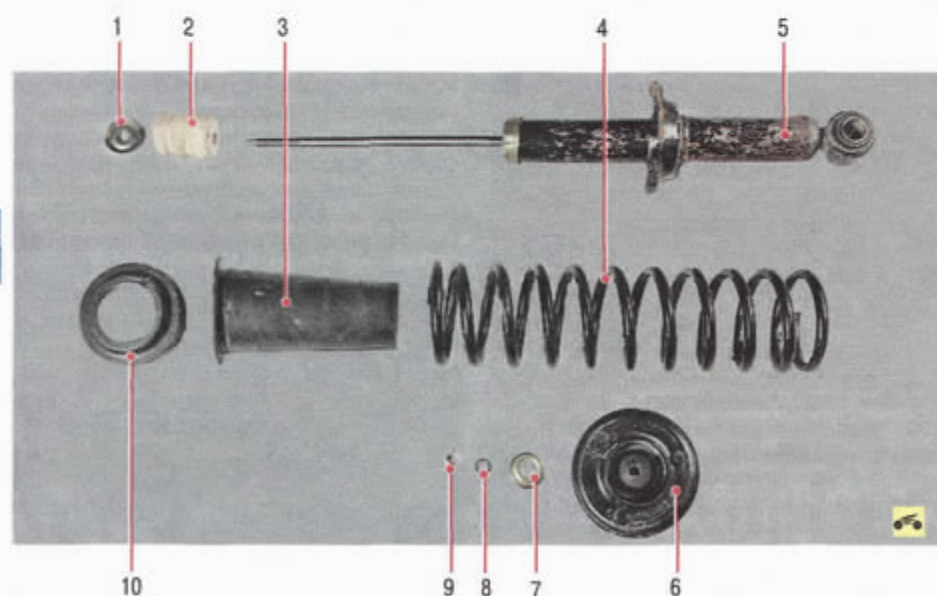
Детали амортизаторной стойки задней подвески: 1, 7 – обоймы; 2 – буфер сжатия; 3 – защитный чехол; 4 – пружина задней подвески; 5 – амортизатор; 6 – верхняя опора амортизаторной стойки; 8 – шайба; 9 – гайка штока амортизатора; 10 – изоляционная прокладка пружины задней подвески
